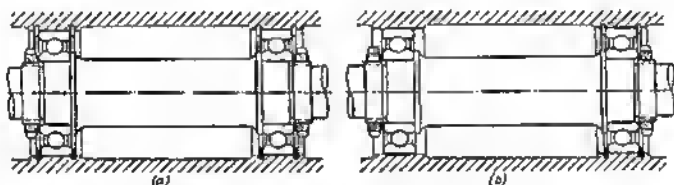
Fijación de un árbol en cojinetes de contacto rodante
